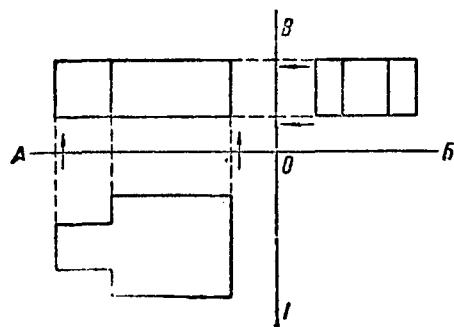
Нахождение фасада шипа по данным профилю и плану.
